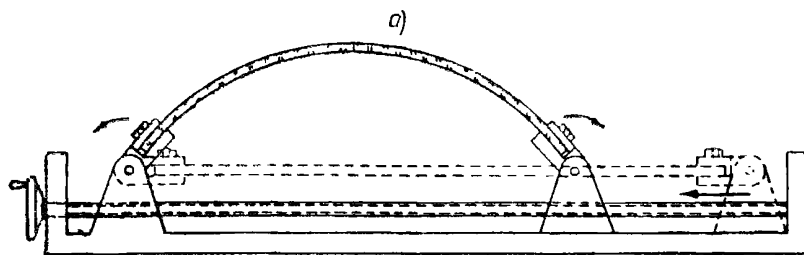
Схема и приспособление для формования деталей одинарной кривизны продольным изгибом:
